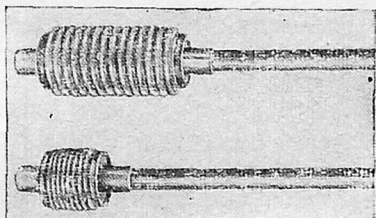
Сильфонные узлы, сваренные аргоно-дуговой сваркой.
